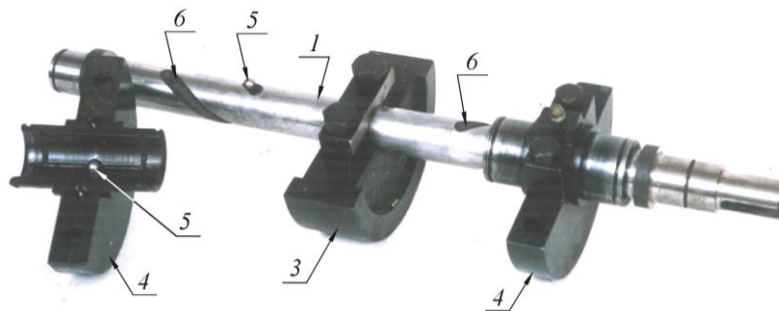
Фото дебалансного вала КМВДЗК (лівий рухомий дебаланс – знятий з вала)
